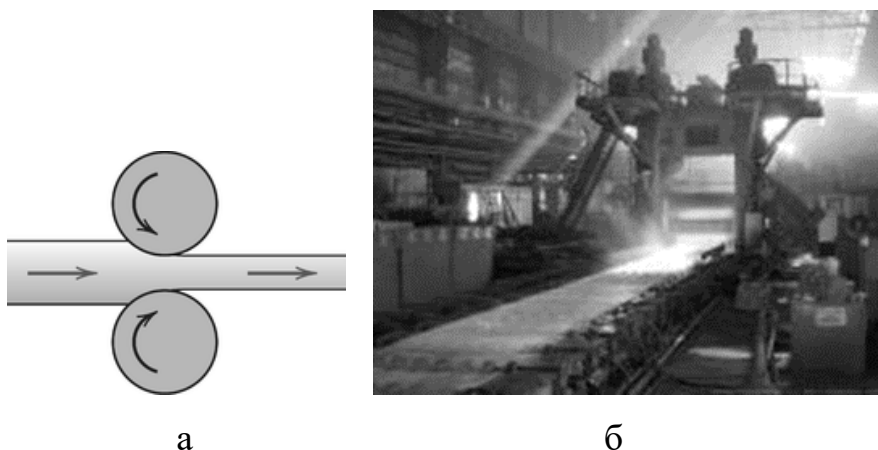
Схема прокатування (а), прокатний стан (б)
